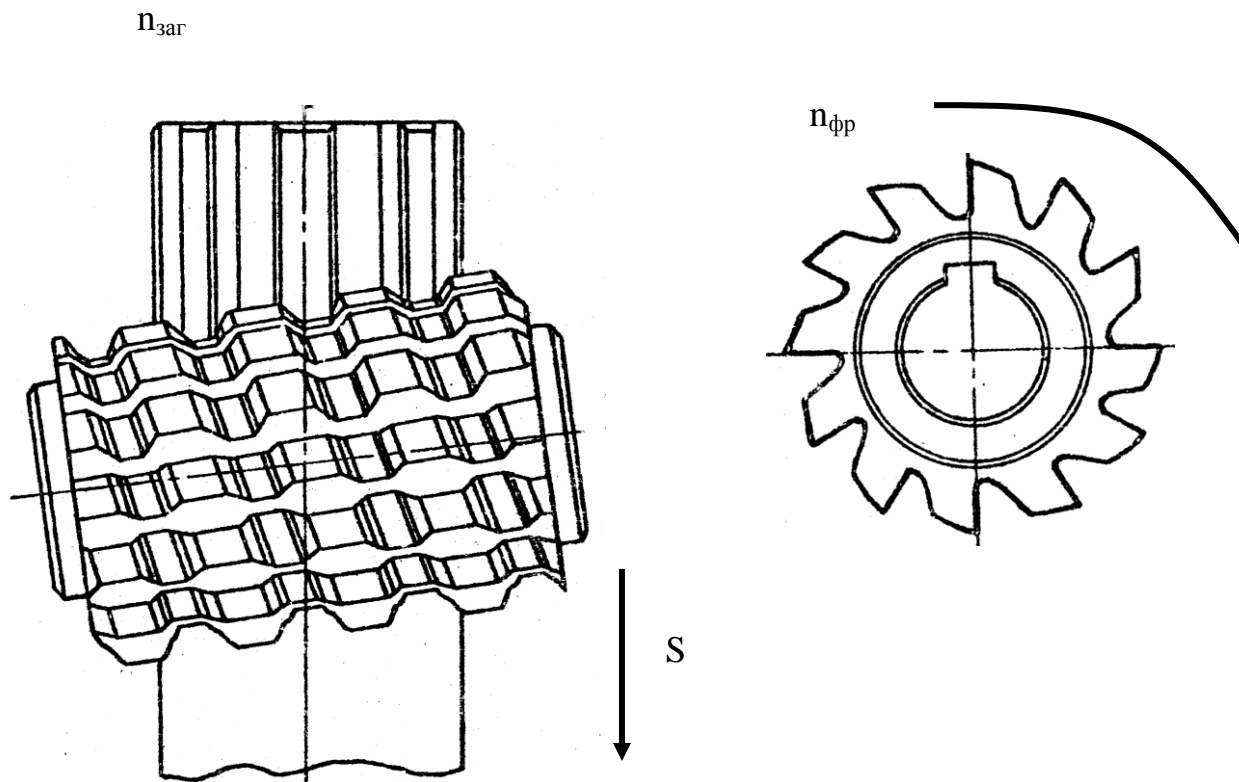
Схема резания червячной шлицевой фрезы:
